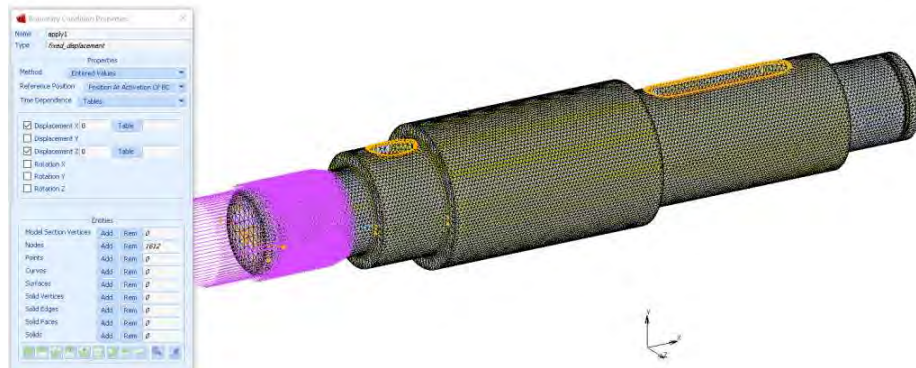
Detalle de la fijación en el apoyo A del eje intermedio
